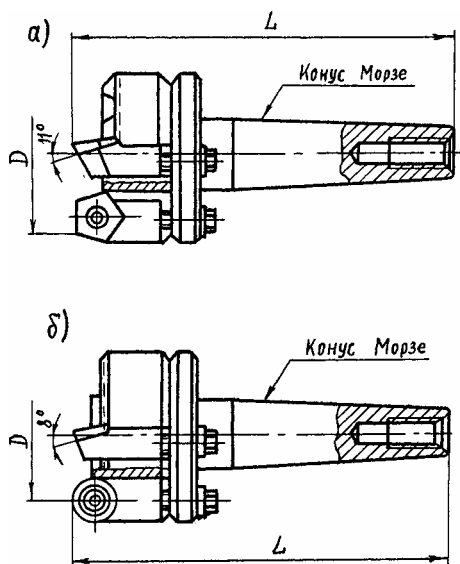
Фрезы торцовые концевые с механическим креплением твердосплавных пластин: а) с пятигранными пластинами; б) с круглыми пластинами
